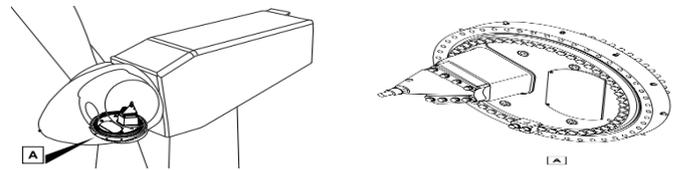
vue générale et emplacement du système de roulement de pale dans le rotor.
